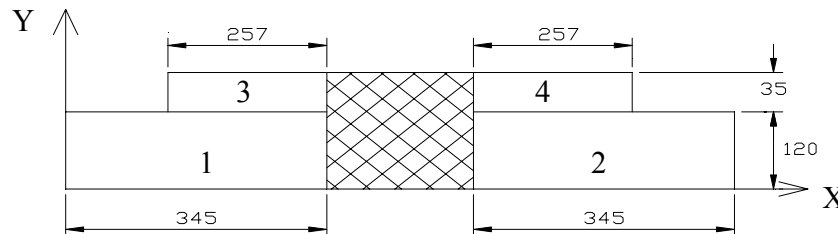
Forma geométrica y principales dimensiones del cubo.
